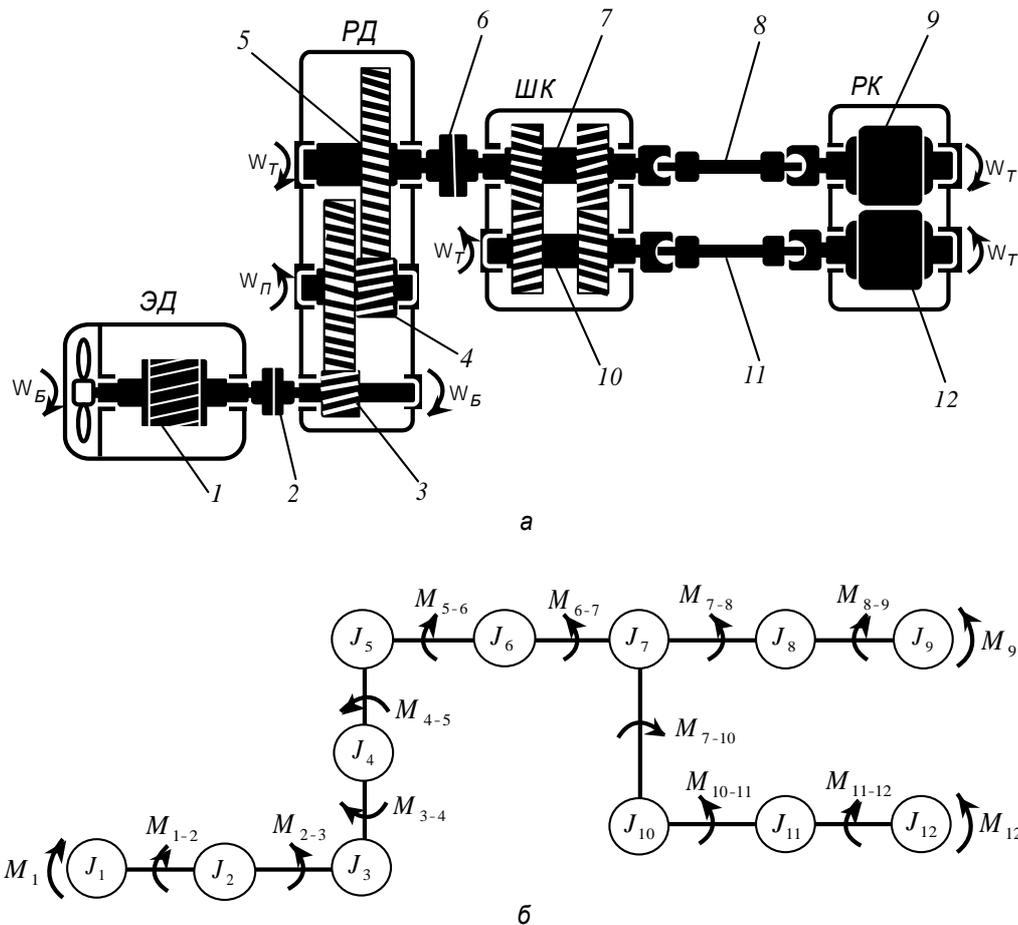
Кинематическая (а) и расчетная (б) схемы электропривода клетки: ЭД – электродвигатель; РД – редуктор; ШК – шестеренная клетка; РК – рабочая клетка; 1 – ротор; 2 – моторная муфта; 3 – быстроходный вал-шестерня; 4 – промежуточный вал-шестерня с зубчатым колесом; 5 – тихоходный вал с зубчатым колесом; 6 – коренная муфта; 7, 10 – верхний и нижний шестеренные валки; 8, 11 – верхний и нижний шпиндели; 9, 12 – верхний и нижний рабочие валки; $\omega_B, \omega_P, \omega_T$ – угловые скорости быстроходного, промежуточного и тихоходного валов
